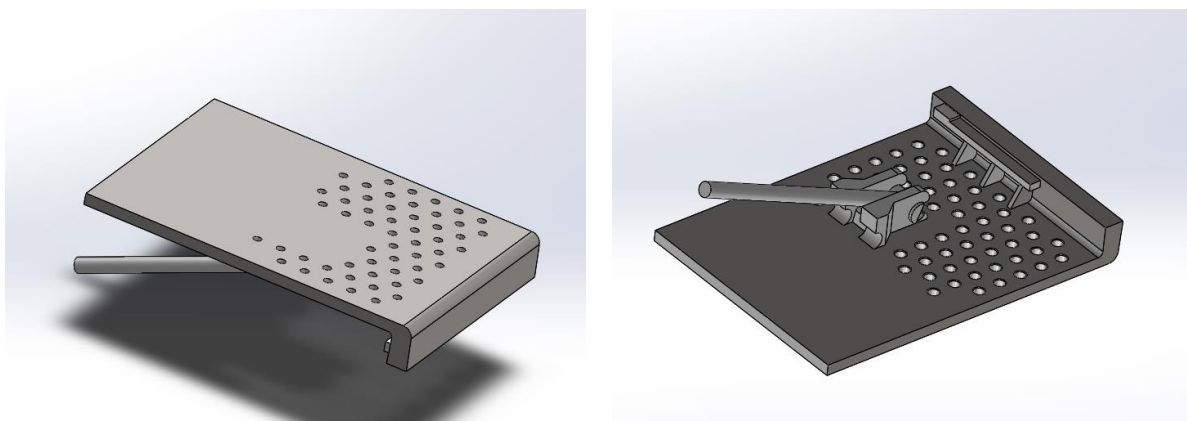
Montagem do Modelo Desenhado da Placa com o Pino de Fixação
